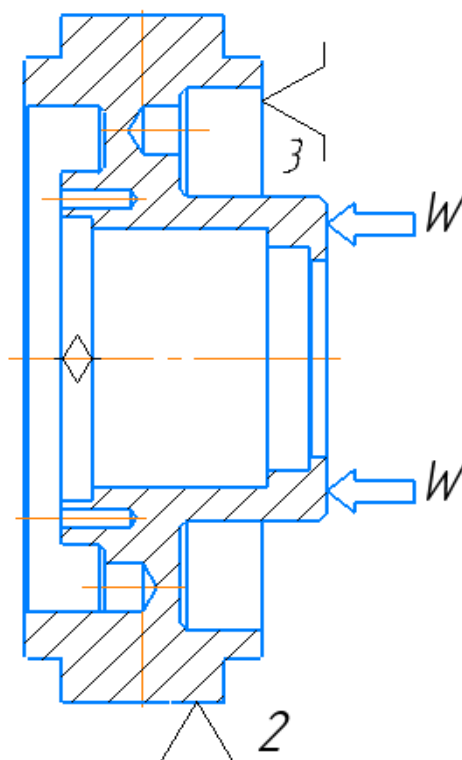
Принципиальная схема зажима заготовки в приспособлении с указанием мест приложения силы зажима.
